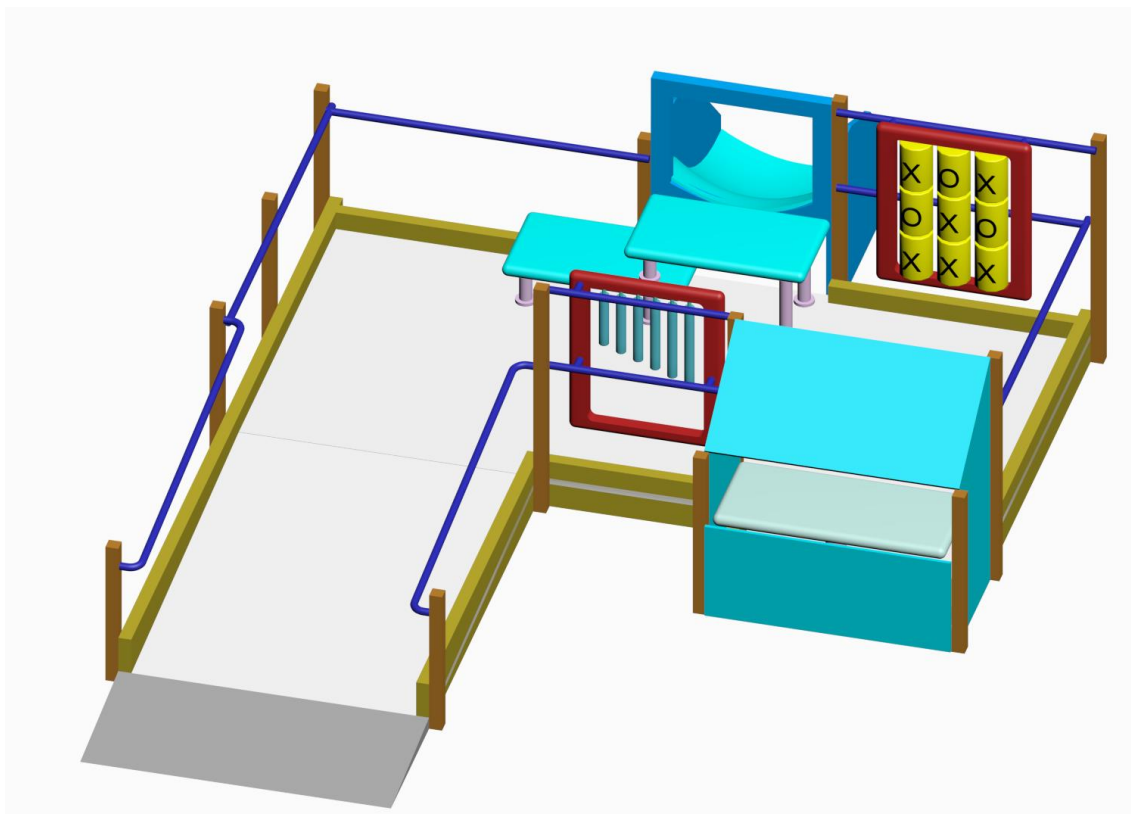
Vista general del elemento multijuego. Fuente: Elaboración Propia
